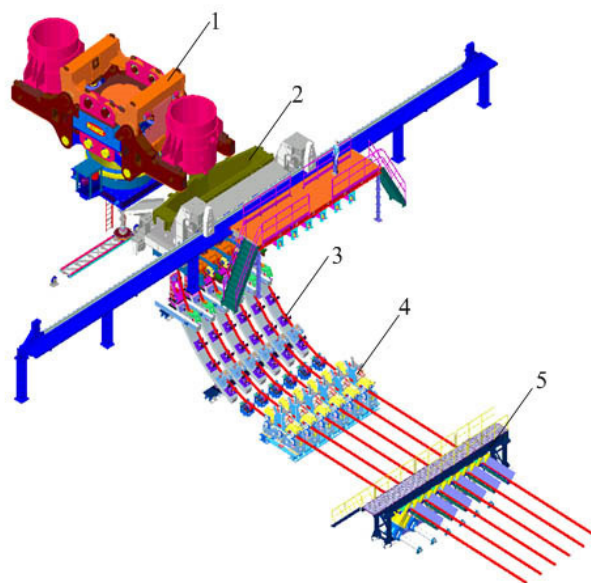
Схема 6-ти ручьевого сортового МНЛЗ: 1 – поворотный стенд со сталеразливочными ковшами; 2 – промковш; 3 – разливочная дуга и ЗВО; 4 – тянуще-правильная машина; 5 – устройство для порезки заготовки
